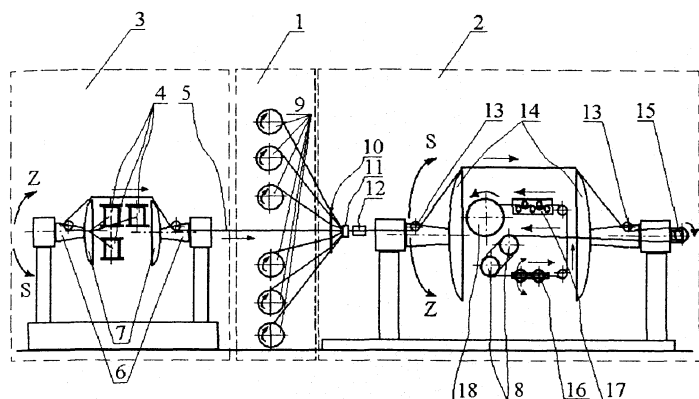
Схема изготовления металлокорда 2+7хd в одну технологическую операцию: 1 – размоточное устройство; 2 – свивочный модуль для готового металлокорда; 3 – свивочный модуль для центральной пряди; 4 – катушки с проволокой для центральной пряди; 5 – центральная прядь; 6 – роторные валы; 7 – роторные диски; 8 – вытяжной кабестан; 9 – катушки с проволокой для наружного повива; 10 – распределительный шаблон; 11 – собирающая втулка; 12 – обжимные плашки; 13 – обводные ролики; 14 – роторные диски; 15 – обводной ролик; 16 – торсион; 17 – рихтовка; 18 – приемная катушка с металлокордом
